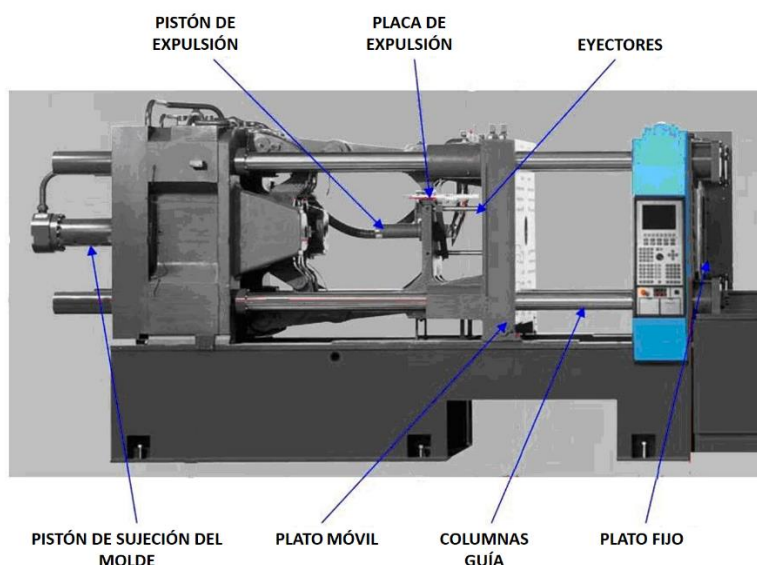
4 Elementos de la unidad de cierre [9]
